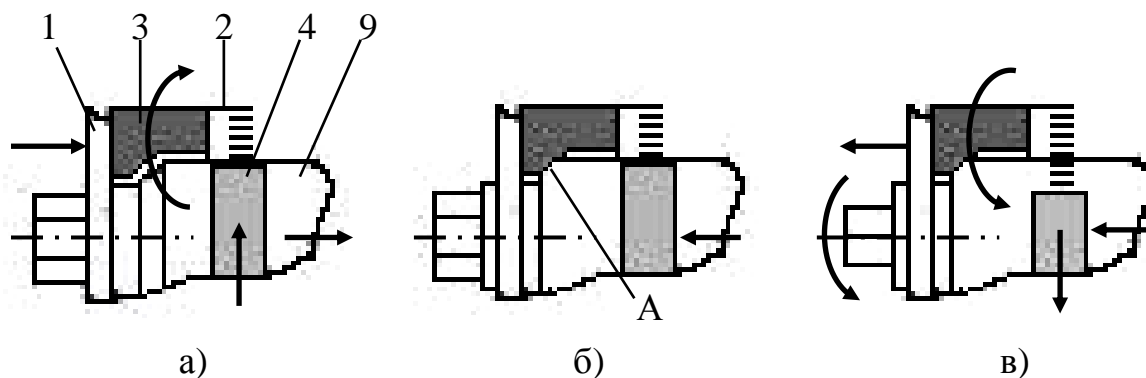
Работа устройства автоматической регулировки зазора между тормозными колодками и барабаном тормозного механизма автомобиля КАМАЗ-6460: а – в процессе торможения, б – начало растормаживания, в – в процессе растормаживания; 1 – корпус рычага регулировочного устройства; 2 – шестерня; 3 – полу муфта наружная; 4 – зубчатая рейка; 9 – вал с червяком; А – поверхности трения
